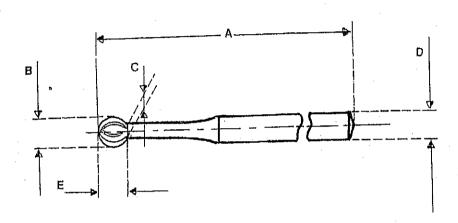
Fresas de carburo, forma redonda (claves: 060.431.0409, 060.431.0417, 060.431.0631, 060.431.0649)
